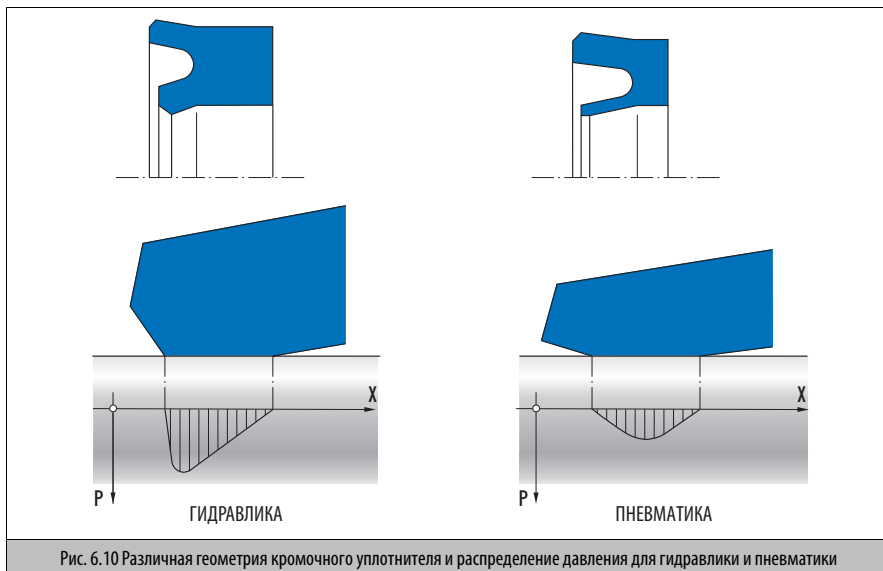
Различная геометрия кромочного уплотнителя и распределение давления для гидравлики и пневматики
